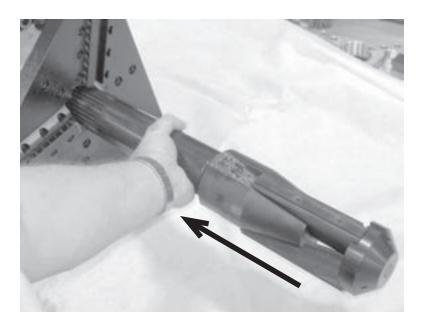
Tirez sur le mandrin pour le sortir de la machine.
